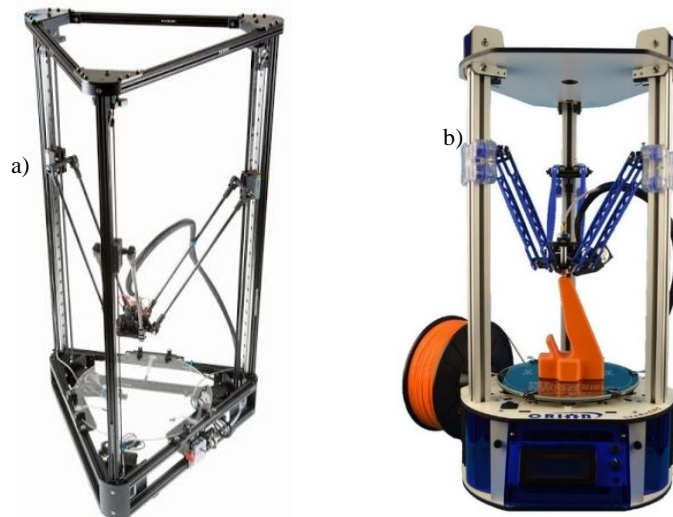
Tipos de chassis de impressoras delta; (a) chassis composto por perfis de alumínio extrudidos [55] e (b) chassis com painéis de melanina [50].
